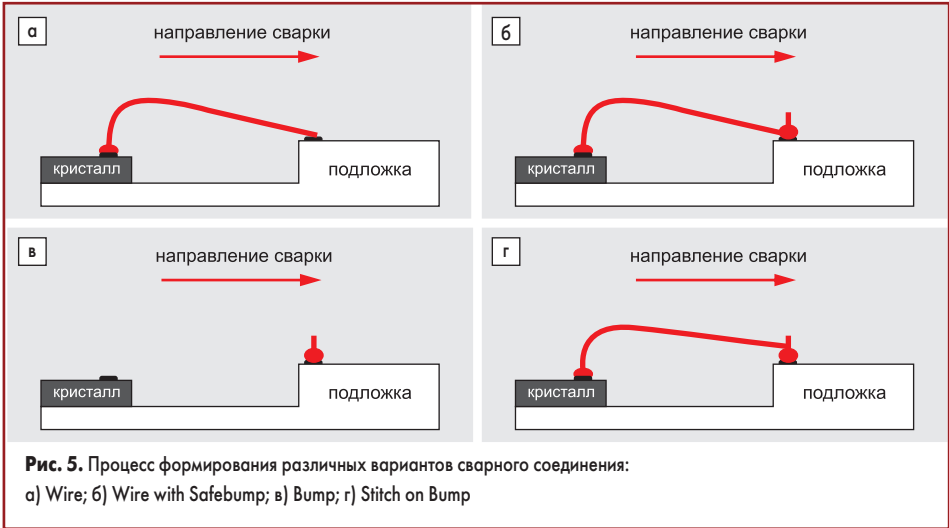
Процесс формирования различных вариантов сварного соединения: а) Wire; б) Wire with Safebump; в) Bump; г) Stitch on Bump
